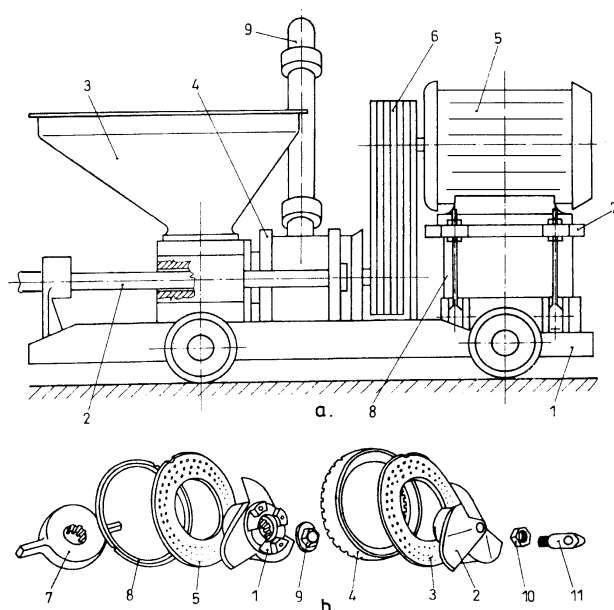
Mașină orizontală de mărunțit fin cu cuțite elicoidale și site
